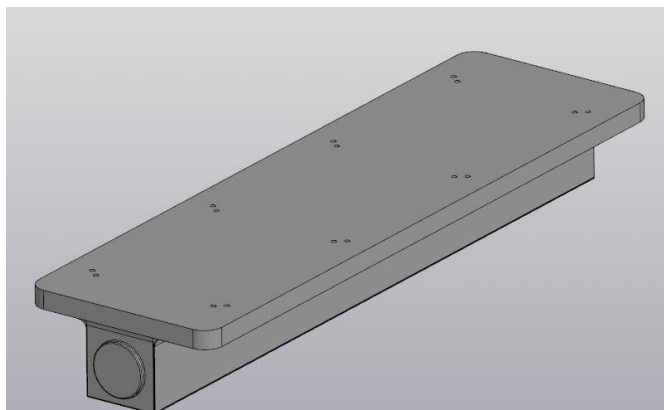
Общий вид 3D-модели корпуса светильника
